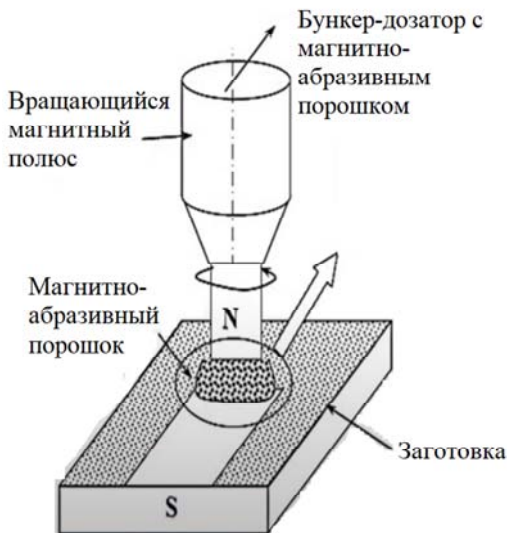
Схема магнитно-абразивной обработки плоских поверхностей
